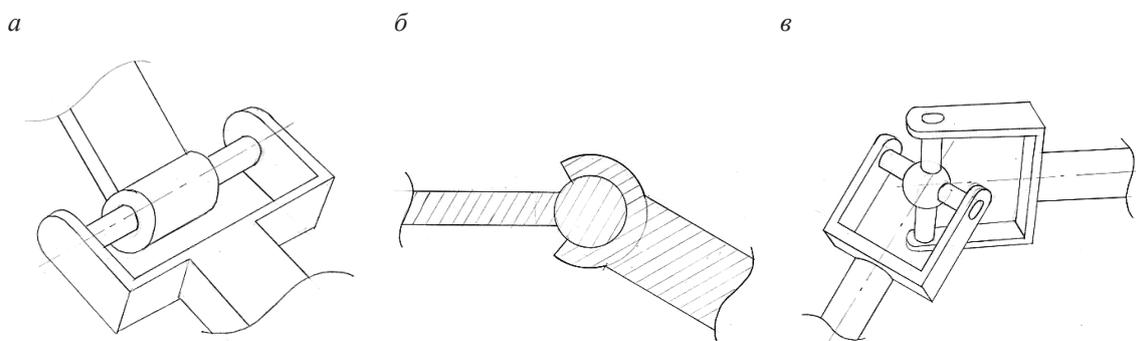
а – цилиндрический шарнир; б – сферический шарнир; в – шарнир угловых осей
